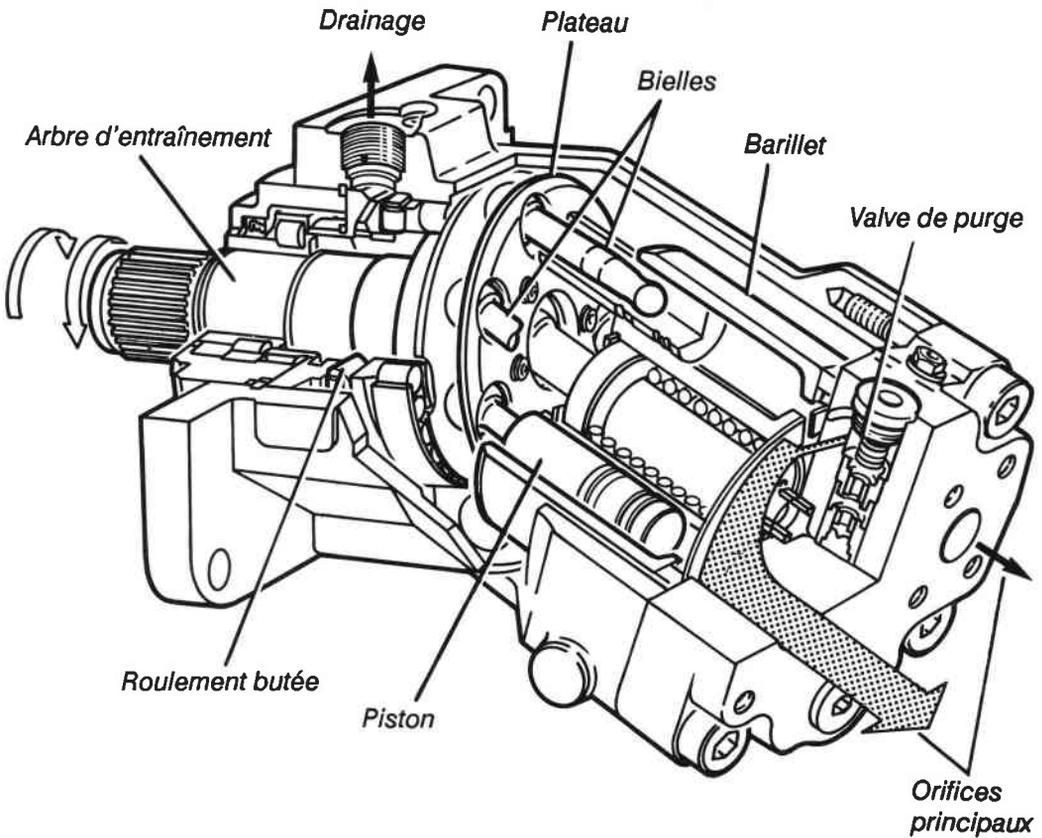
Moteur hydraulique à barillet oblique et cylindrée fixe
